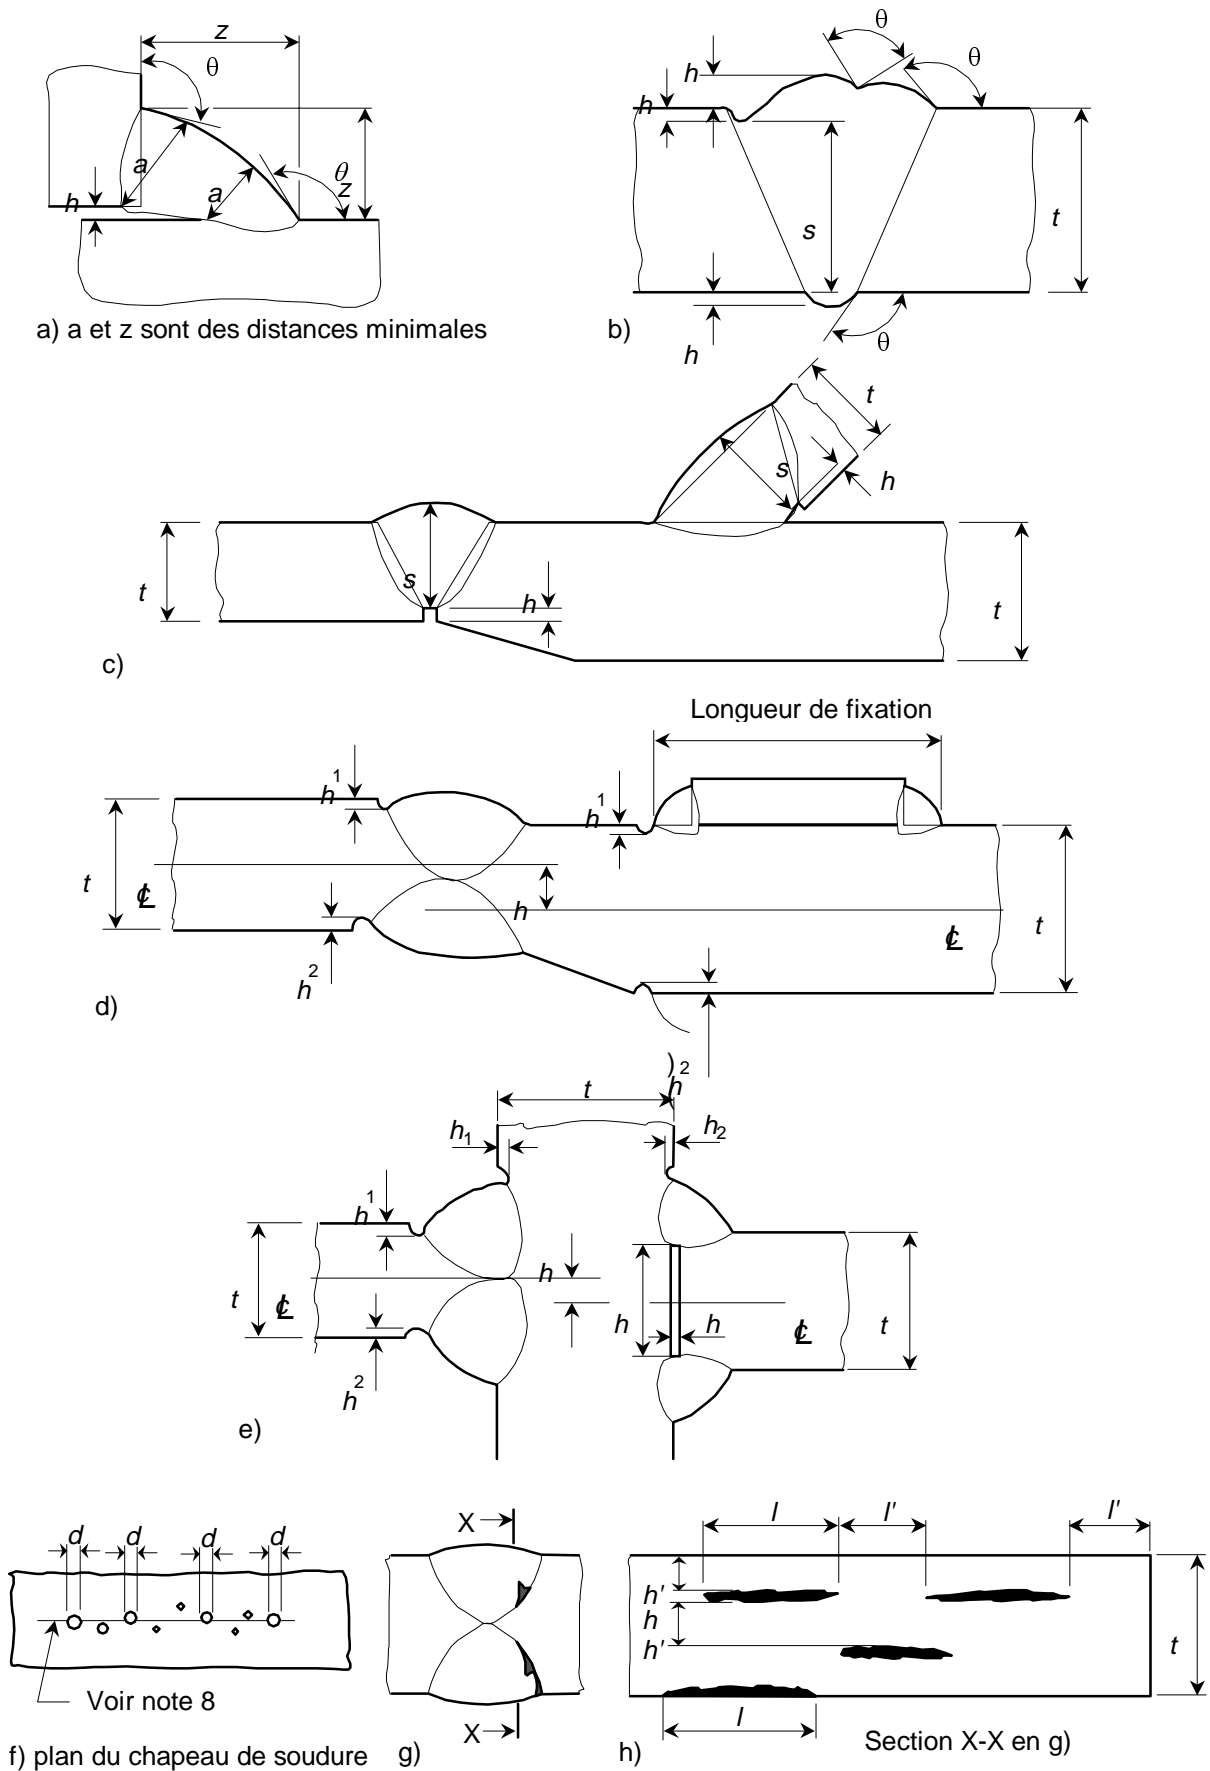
Dimensions des discontinuités de soudure
